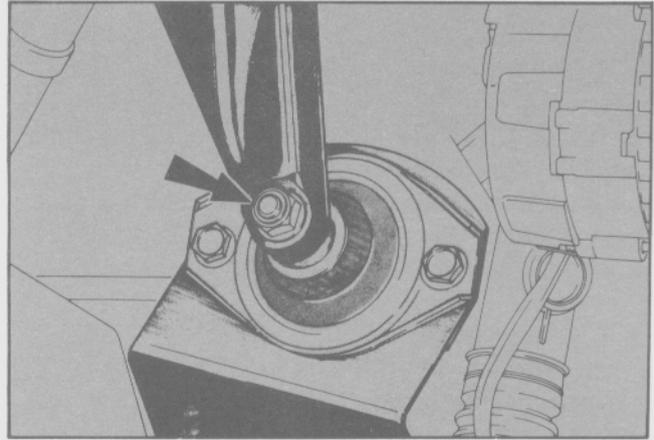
Tuerca de fijación del soporte de montaje del motor al aislador
